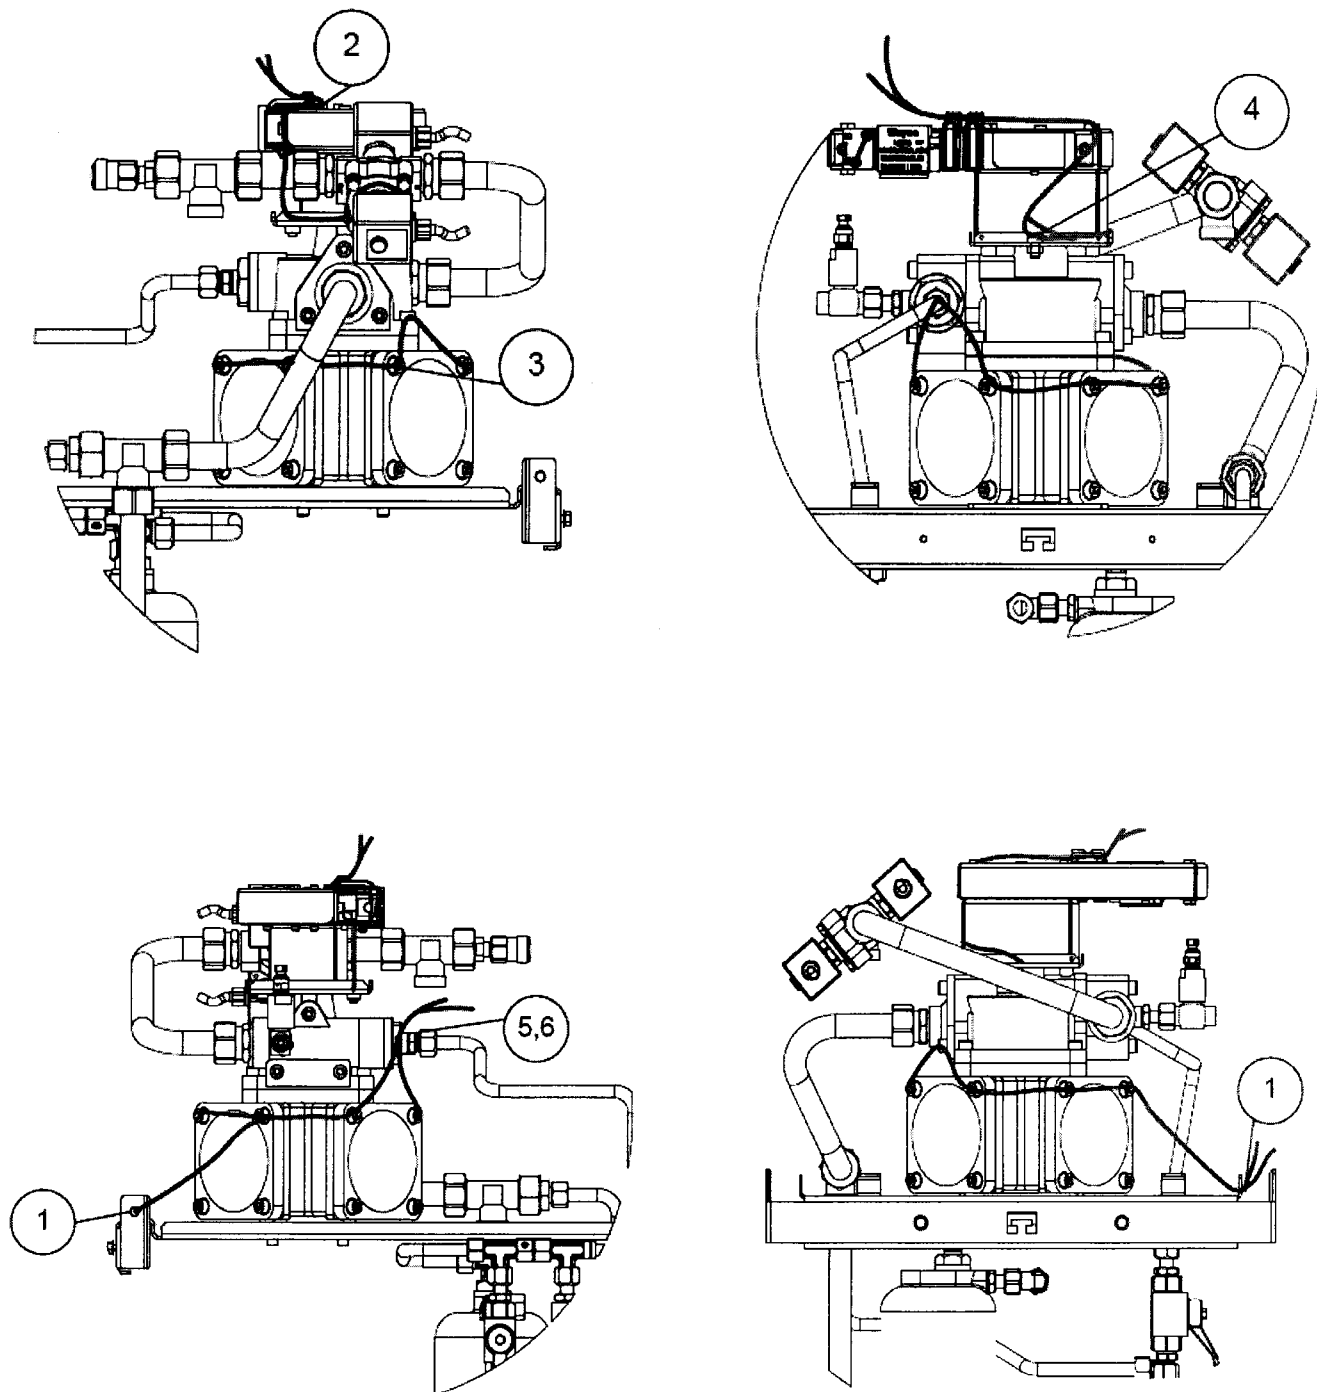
Схема нанесения знака поверки на LPG6000
